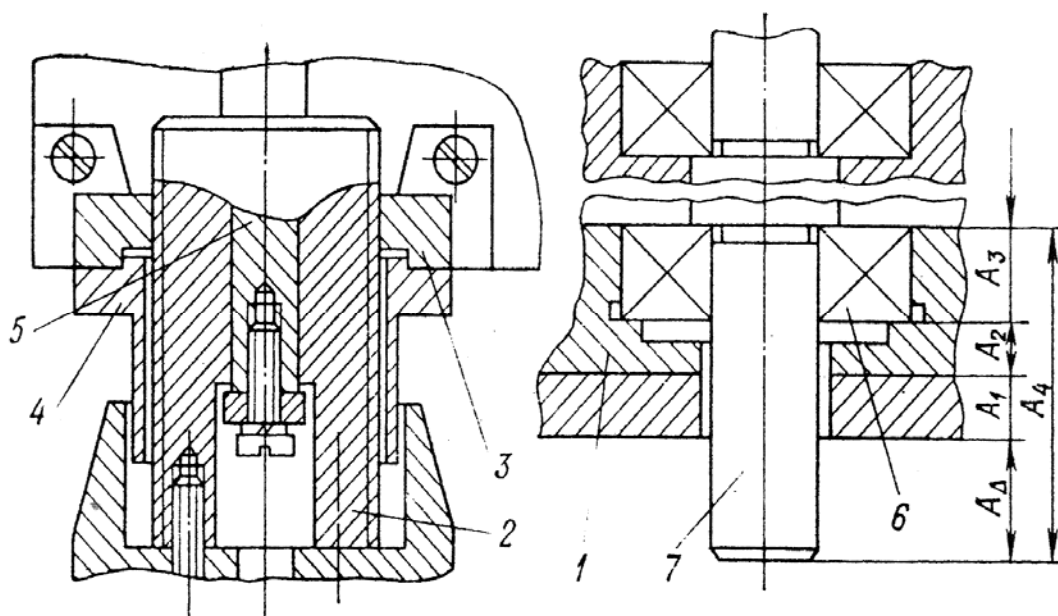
Узел подшипникового соединения: 1 – стакан; 2 – винт; 3- кронштейн; 4 – втулка; 5 – ось; 6 – подшипник; 7 – вал
